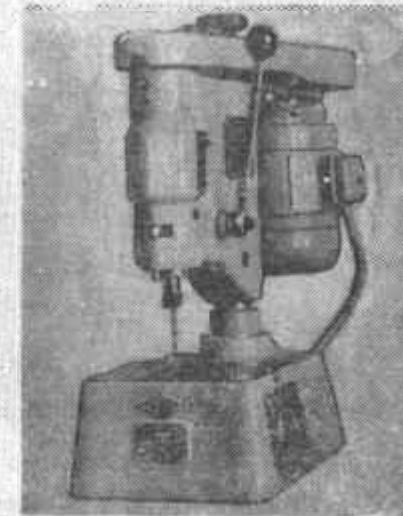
Настольный вертикально-сверлильный станок модели C155
